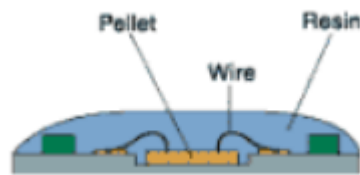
Безкорпусний монтаж (Chip On Board) КЕ на ДП
